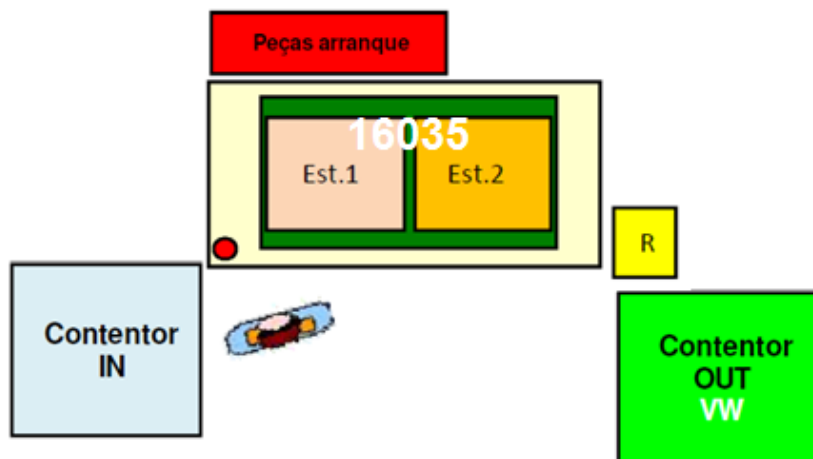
Layout da prensa de soldadura de 150 KVA (operação 90);
